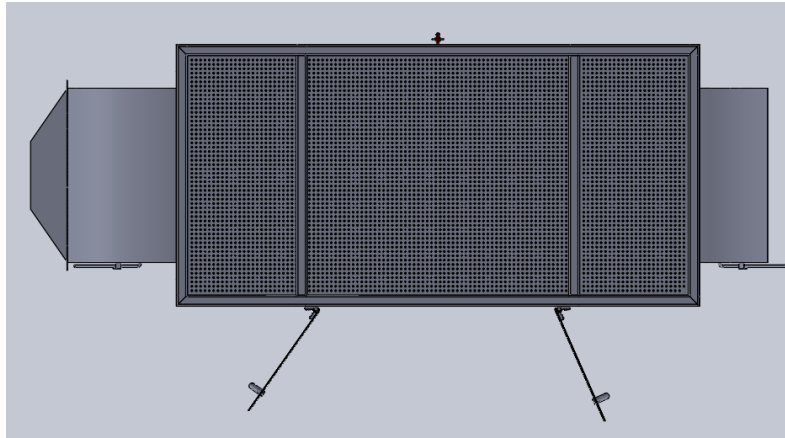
Vista de planta de sistema de apertura con puertas y bisagras.
